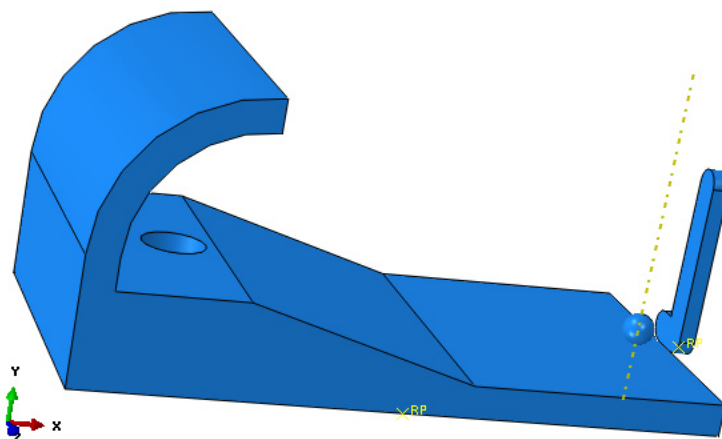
Wybór punktów względem pierwszej translacji elementu *Kij
